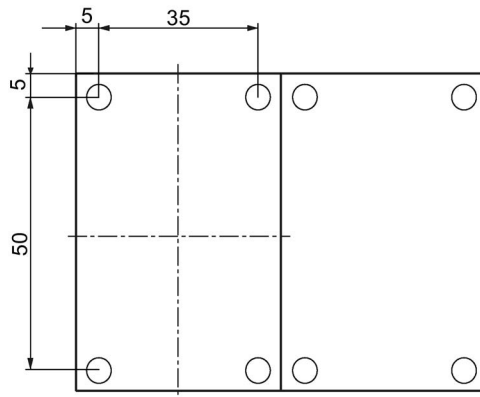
Bohrplan der Wendekombinationen 3RA231.-8X.3.-1 (Baugröße S00, Schraubanschlusstechnik)
